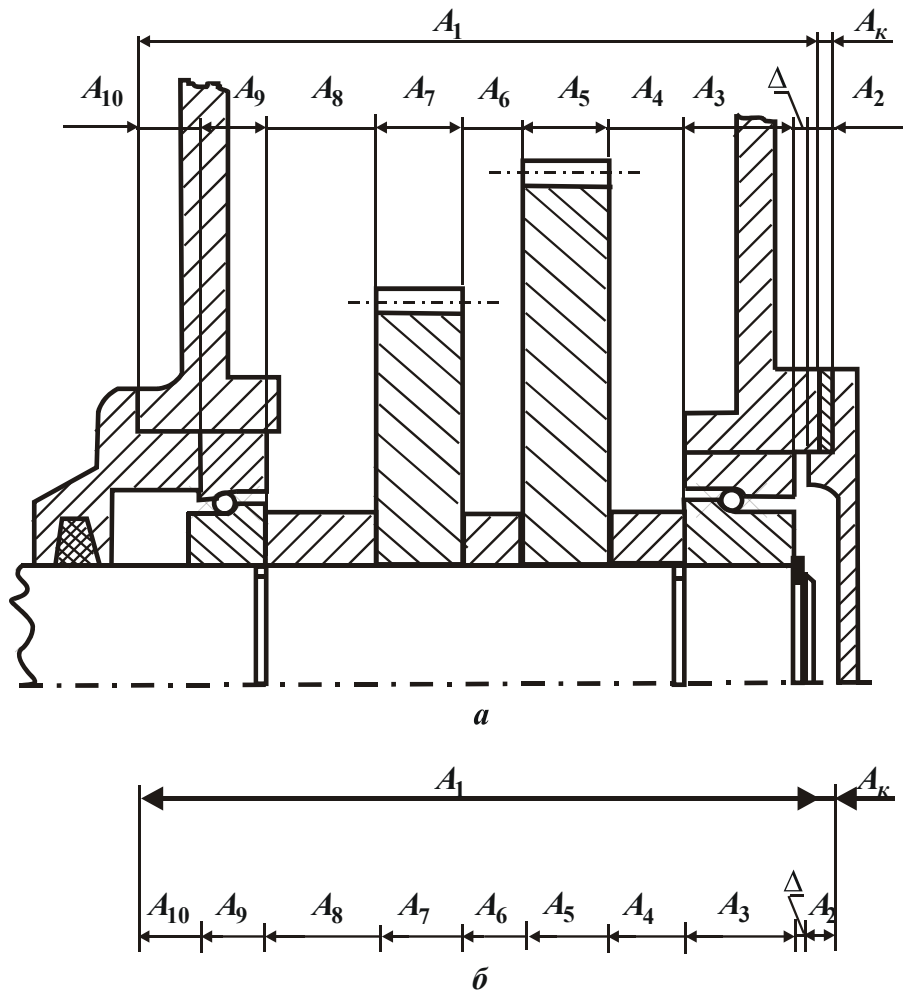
Схемы: а – осевого разреза корпуса редуктора; б – размерной сборочной цепи.
